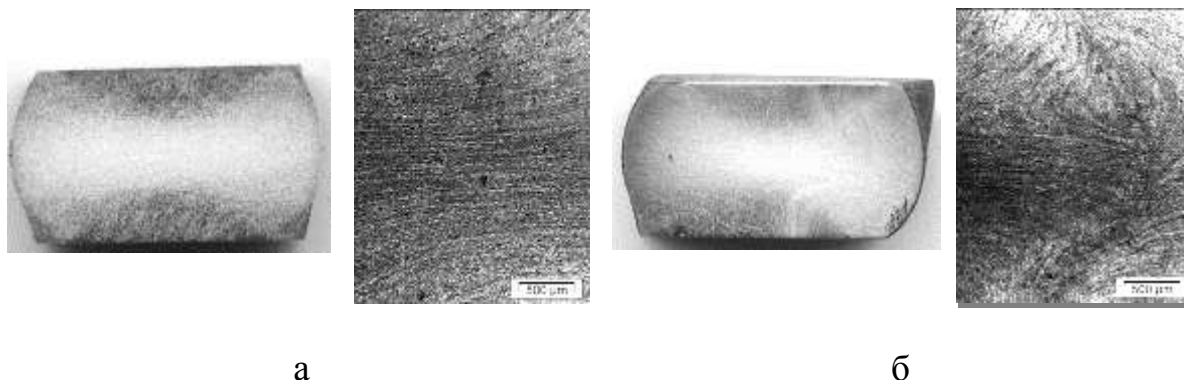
Типичные макро- и микроструктуры образцов после осадки: а – образец без сварного соединения, б – образец со сварным соединением)
